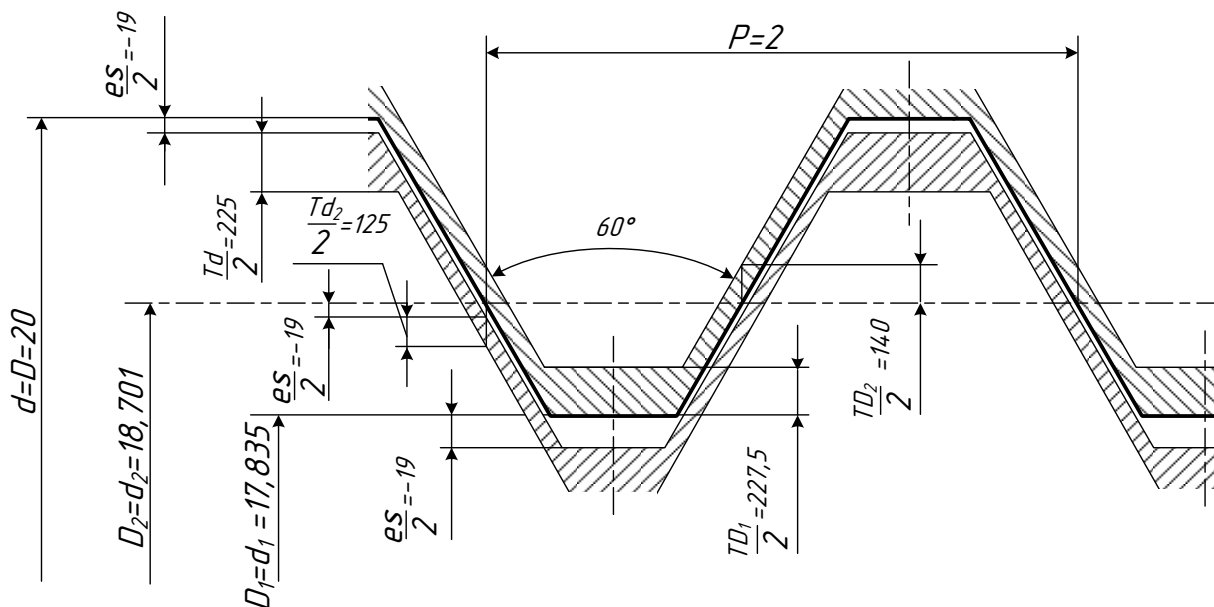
Схема расположения полей допусков резьбового соединения
